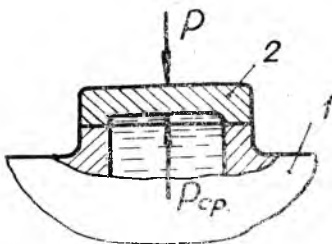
Схема соединения деталей с плоской металлической уплотняющей поверхностью:
